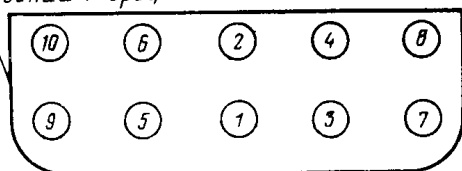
Последовательность затяжки гаек крепления головки цилиндров
